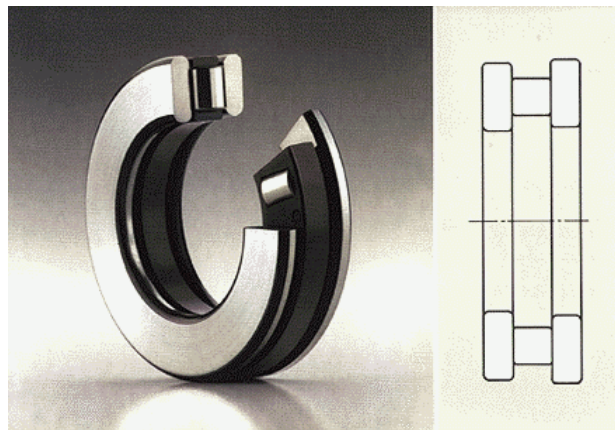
Rodamiento axial de rodillos cilíndricos
